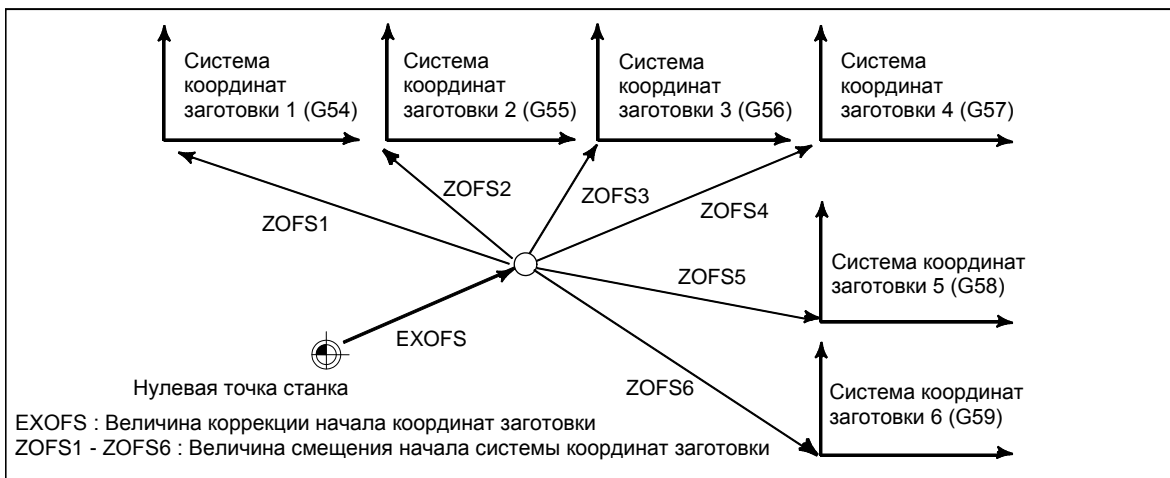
(а) Изменение значения внешней коррекции начала координат заготовки или значения коррекции начала координат заготовки
